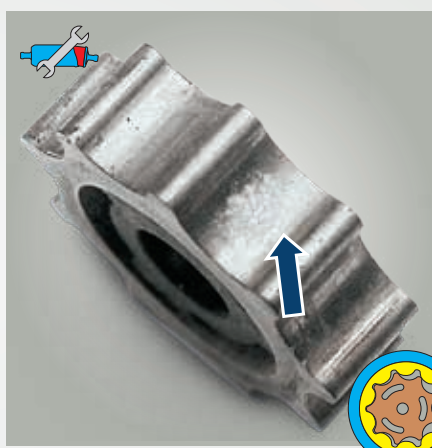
Трохоидное зубчатое колесо с известковыми отложениями
